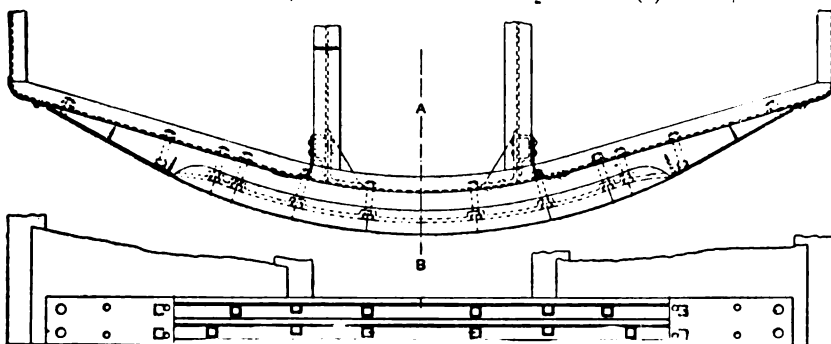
, 83 e 84. — Apparecchio Hedley - Elevazione e pianta.
